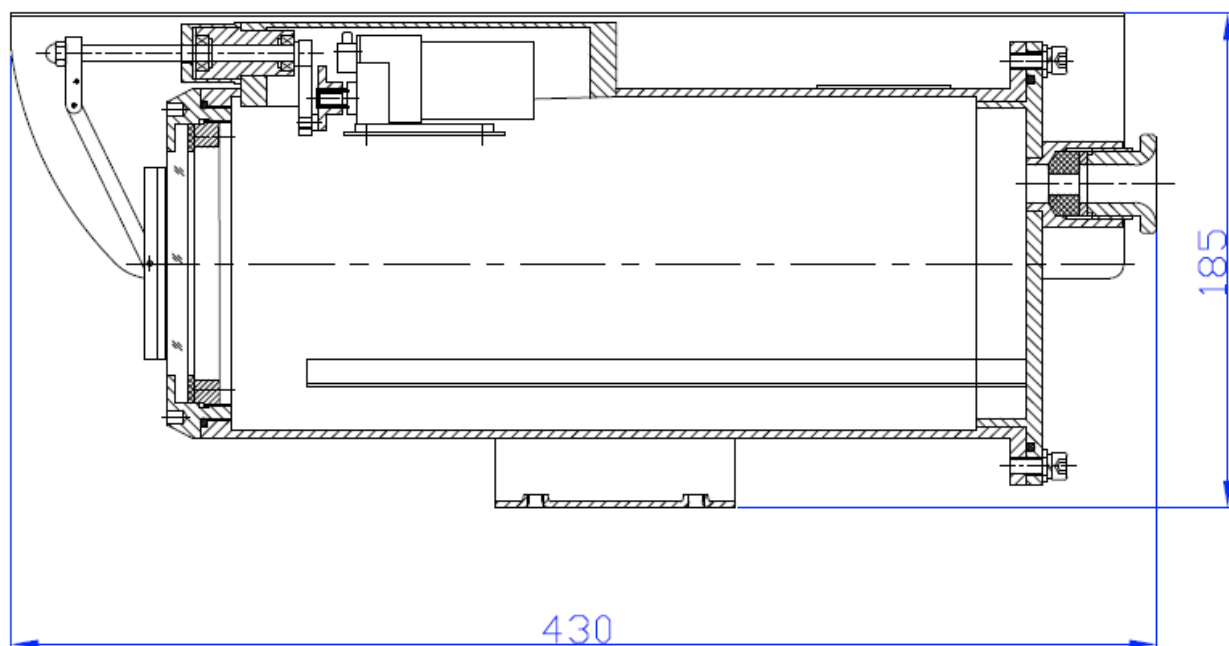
Габаритные размеры TKNCL-9, вид в разрезе
